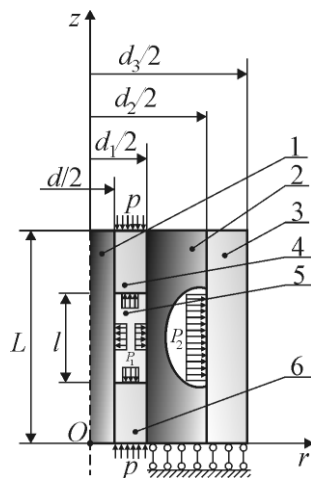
Расчетная схема устройства для прессования полых изделий из порошков: 1 – центральный стержень; 2 – вкладыш; 3 – матрица; 4,6 – пуансоны; 5 – брикет из порошка
